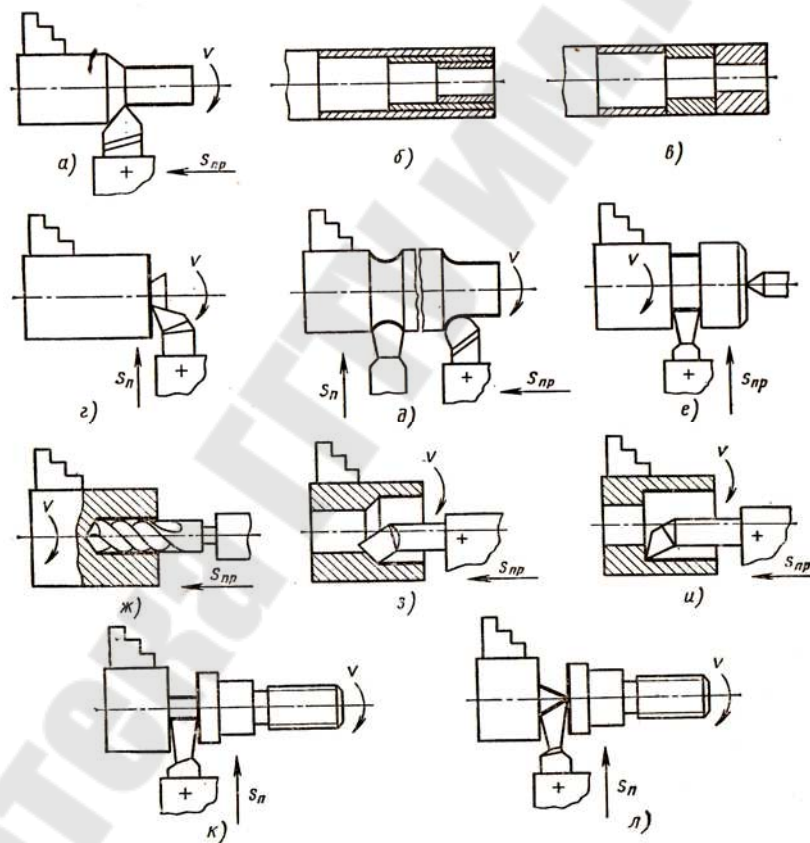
Схемы обработки заготовок на токарно-винторезном станке
